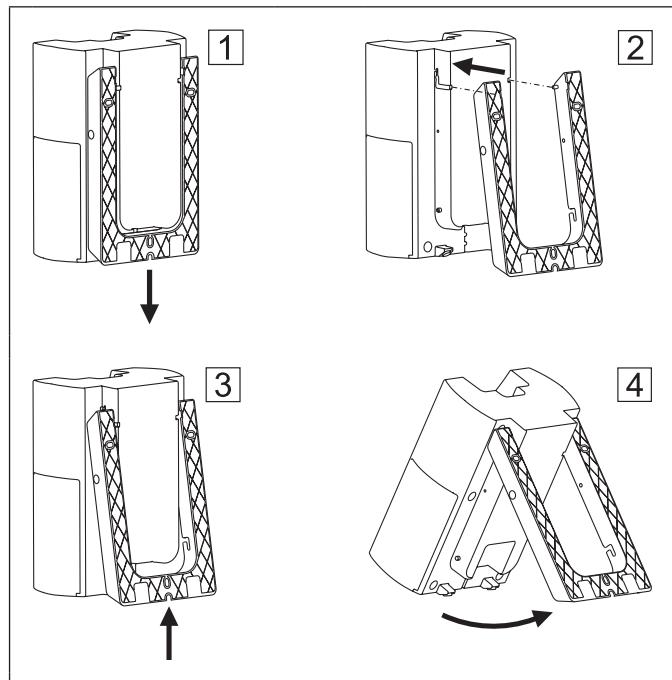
Instalar el equipo de ensayo en posición inclinada (en la figura, el equipo de ensayo se muestra sin soportes y sin bloqueo)
